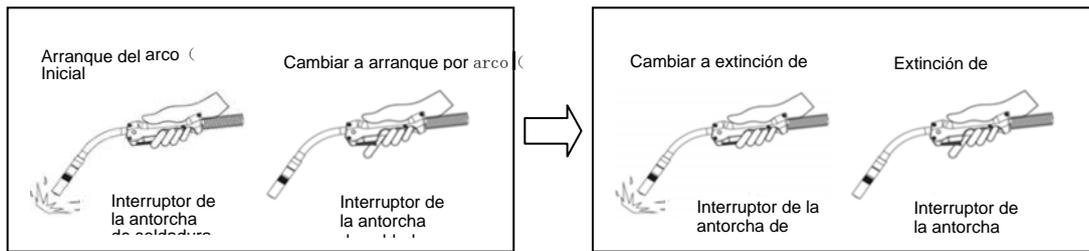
Diagrama de la soldadura especial en modo de cuatro pasos
